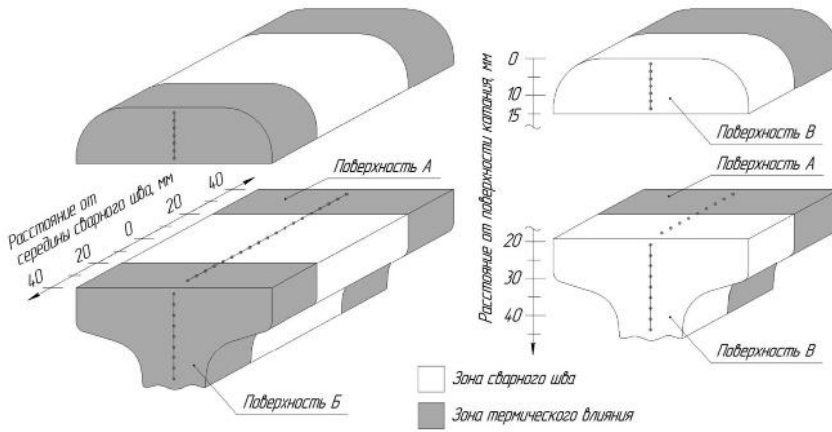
Схема расположения поверхностей и мест нанесения отпечатков при измерении твердости головки рельса алюминотермитного сварного соединения
